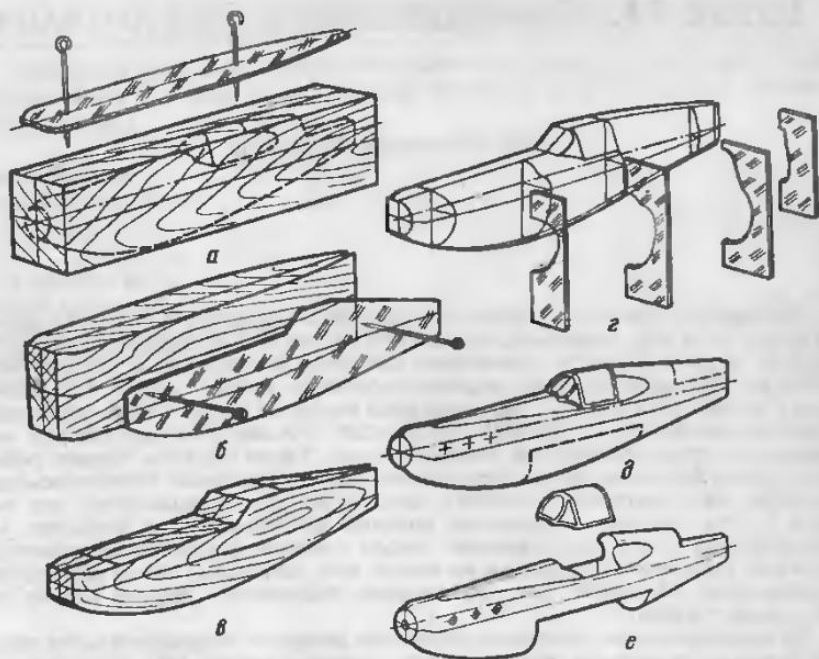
Последовательность изготовления фюзеляжа модели одноместного истребителя: а - разметка болванки "вид сверху"; б - разметка болванки "вид сбоку"; в - полученная заготовка; г - обработка заготовки по шаблонам поперечных сечений; д - разметка; е - разделка фюзеляжа по местам технологических стыков
